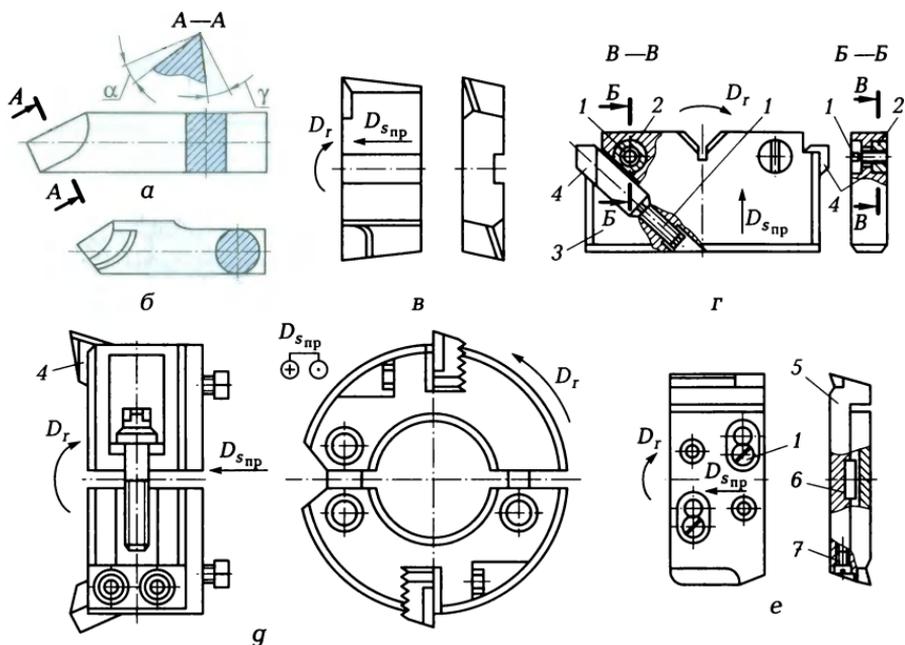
Режущий инструмент для растачивания отверстий:
